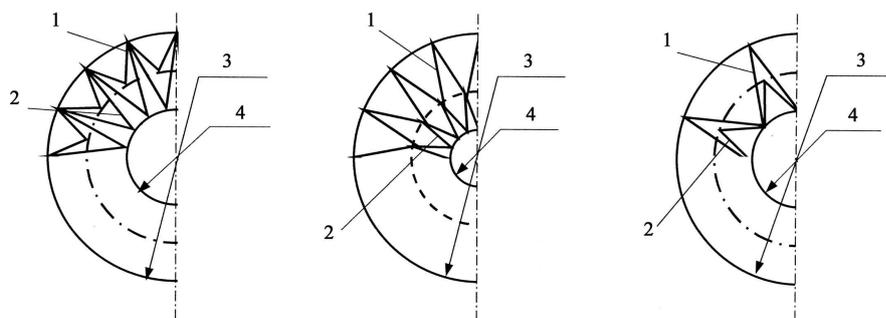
Схема двухступенчатого фильтрующего элемента с звездообразной шторой: 1 – первая ступень очистки; 2 – вторая ступень очистки; 3 – обечайка; 4 – перфорированный каркас
